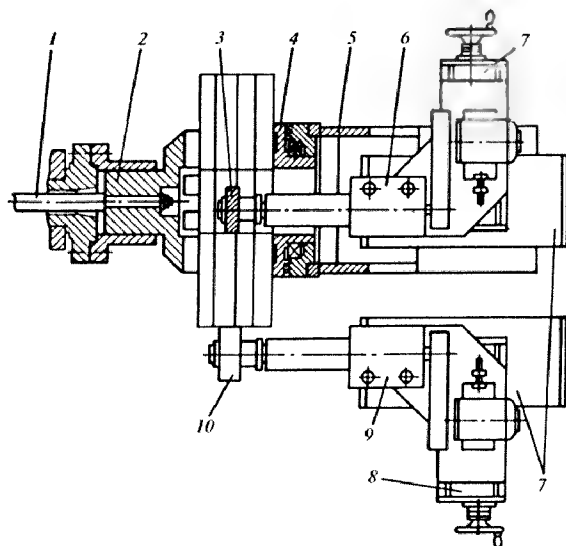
Схема станка модели РТ-103 после модернизации (вид сверху):
